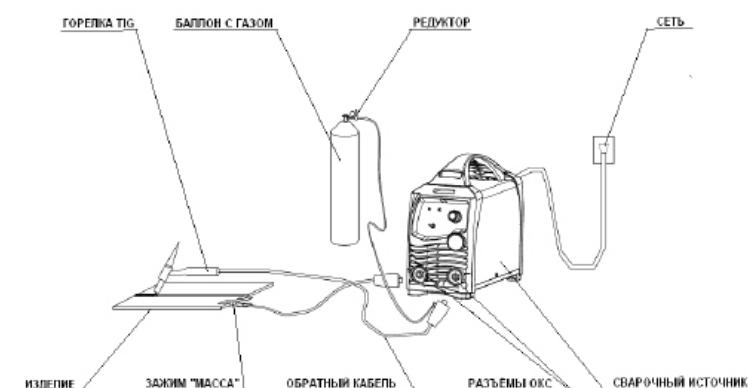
Схема подключения оборудования для TIG сварки
